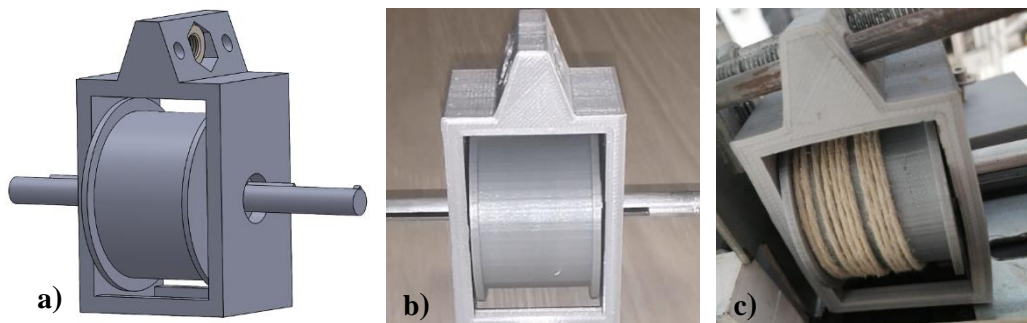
a) Desenho 3D suporte do tambor b), c) Resultado do suporte do tambor
